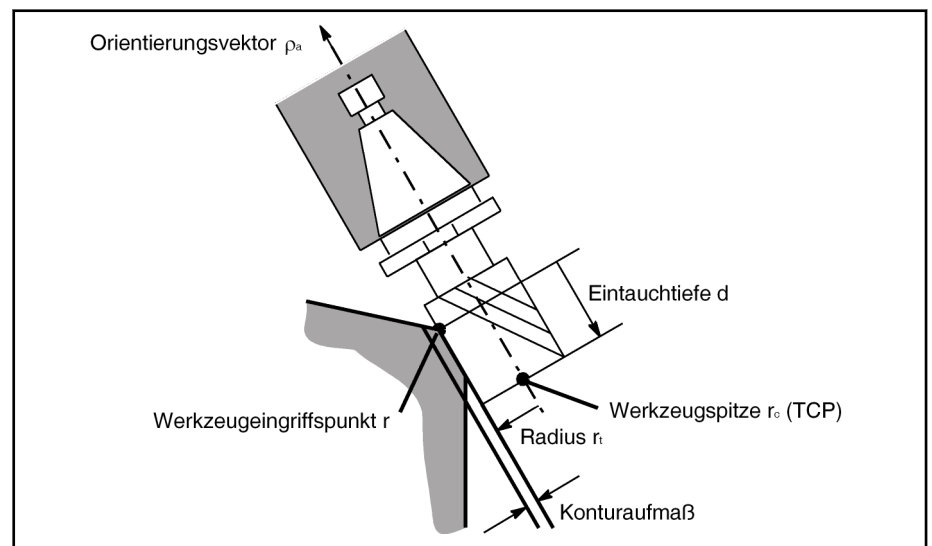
3D-Werkzeugradiuskorrektur
